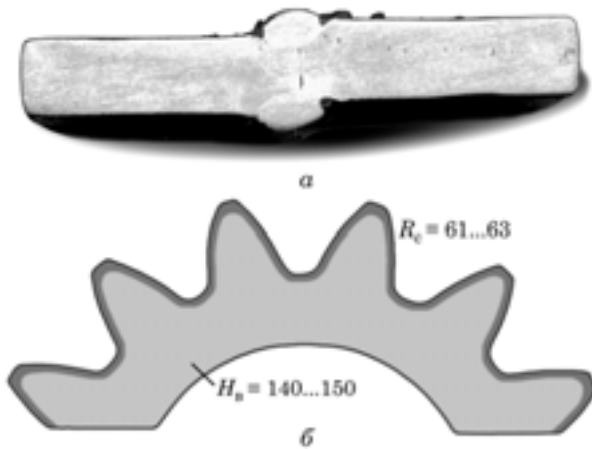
Макроструктура поверхні: а — зварного шва; б — шестерні
